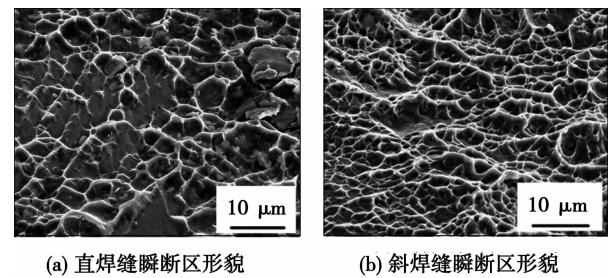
激光直、斜焊缝试件疲劳瞬断区断口形貌
